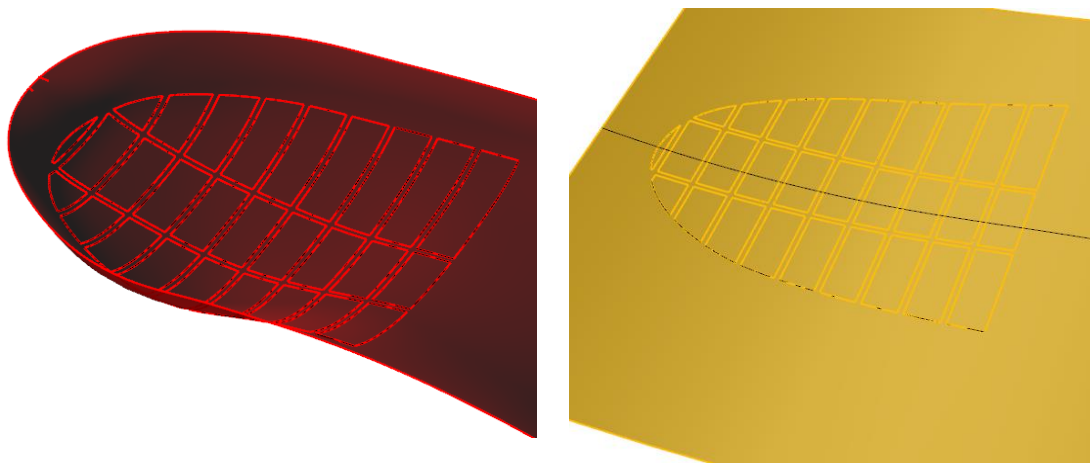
Estructuras 2D proyectadas sobre las superficies límite
